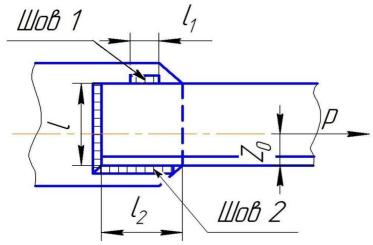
Схема сварного соединения стальных уголка и косынки
